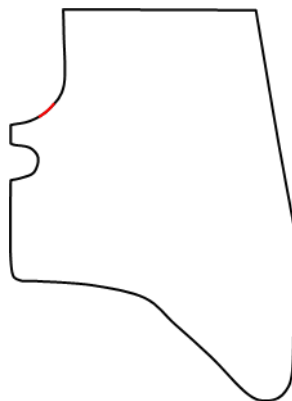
Сечение кольца для аргоно-дуговой сварки
